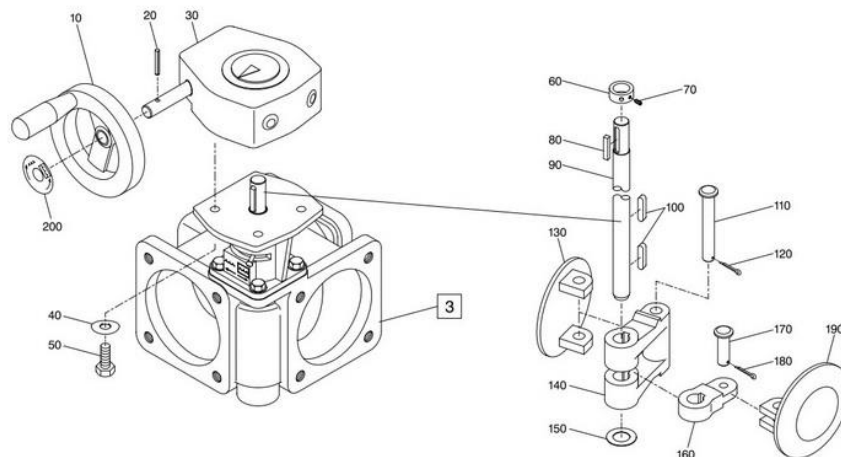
Комбинированная задвижка «Из цистерны» пожарного насоса Zigler
